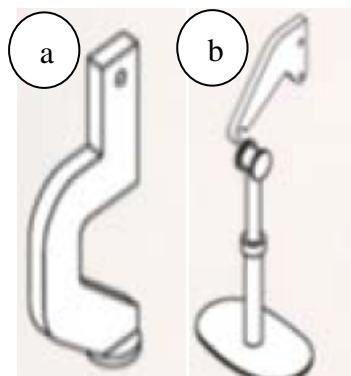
a) Flanco; b) Banda de rodadura y hombro.
